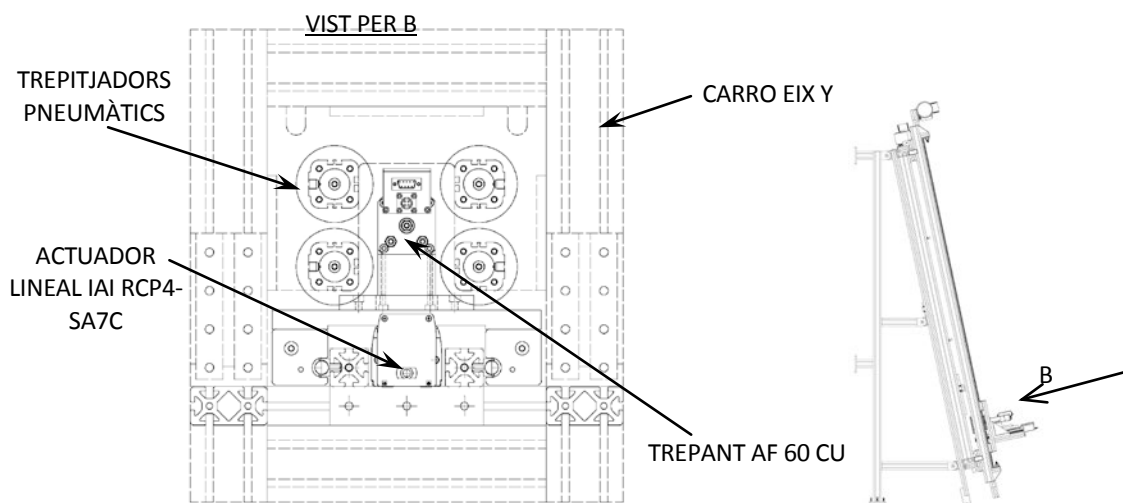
Vista en planta de l'eix Z muntat al carro Y
